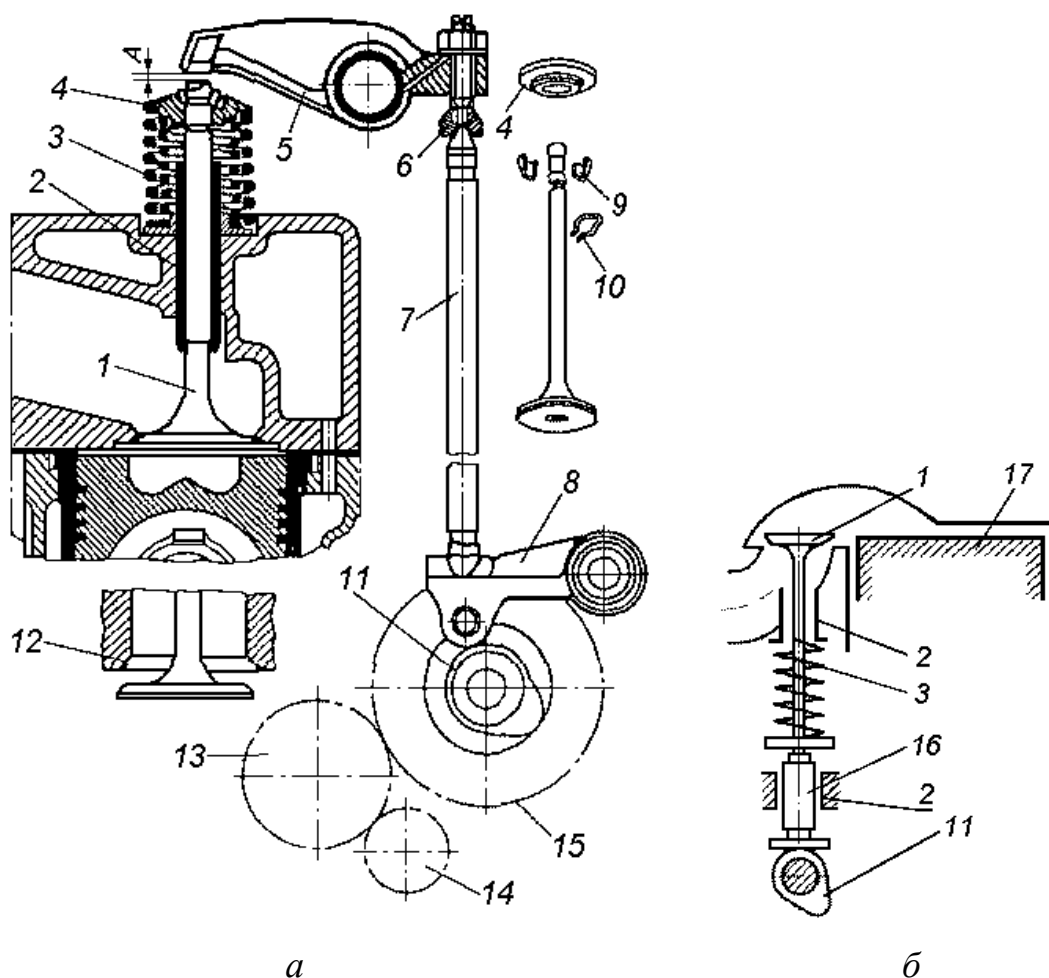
Газораспределительный механизм четырехтактного двигателя:
